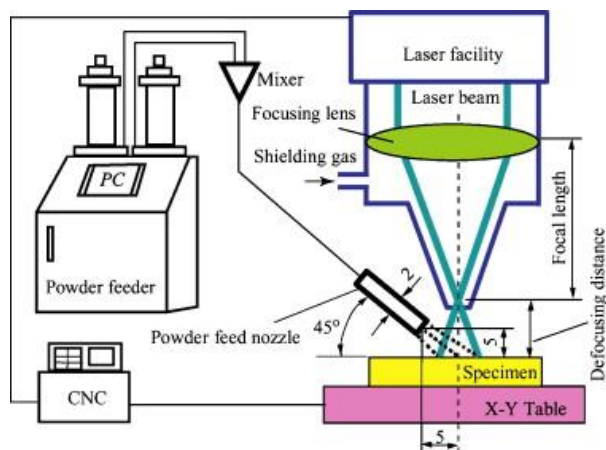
Setup utilizado num processo de LASER cladding [38]
